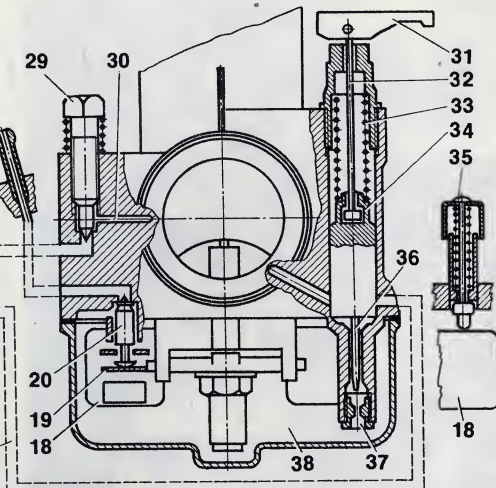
Карбюратор К63Т: 1 — шпунт с контргайкой; 2 — пружина дросселя; 3 — ограничитель подъема дросселя; 4 — крышка корпуса; 5 — контргайка; 6 — планка дозирующей иглы; 7 — дроссель; 8 — корпус; 9 — воздуш-
